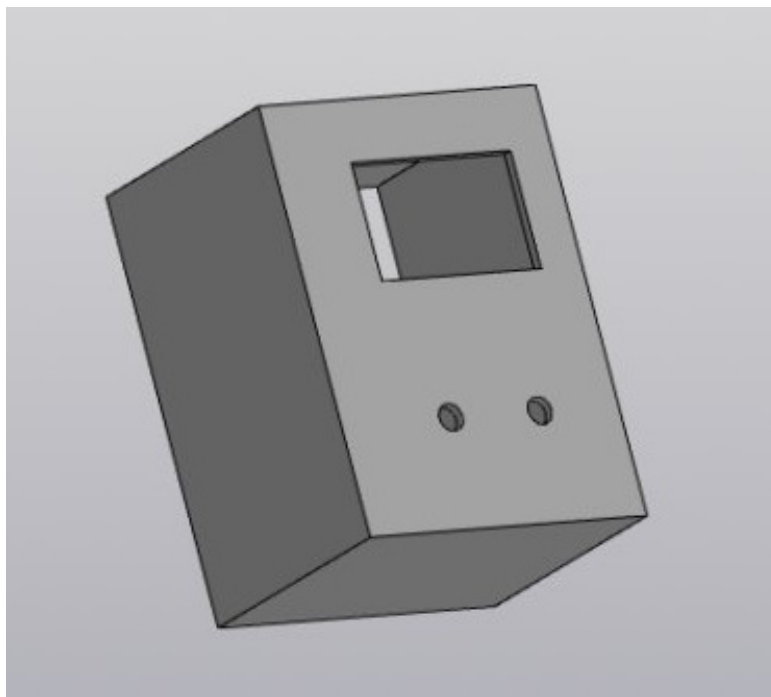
Основна частина корпусу приладу, вигляд спереду.
